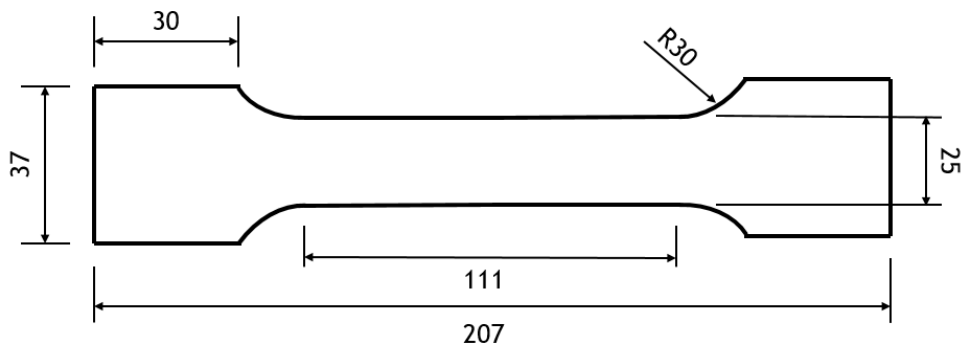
Dimensões dos provetes em [mm] para teste de tração em solda.
